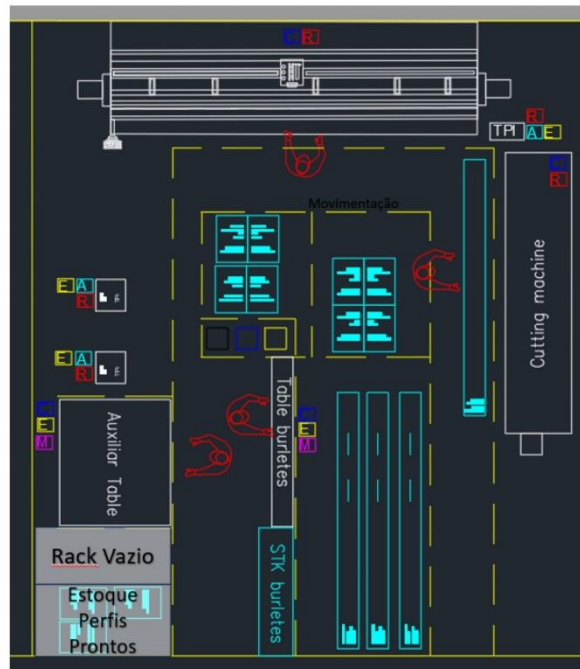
Setor de Corte e Maquinagem de Perfis
